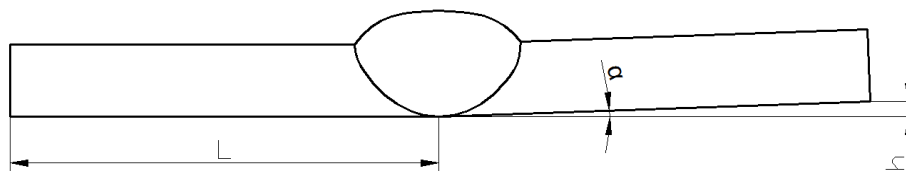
Размеры угловой деформации стыкового сварного шва:
